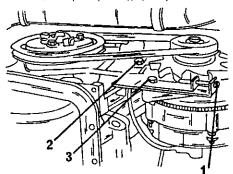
Регулировка натяжения ремня генератора переменного тока (двигатель типа TU).
